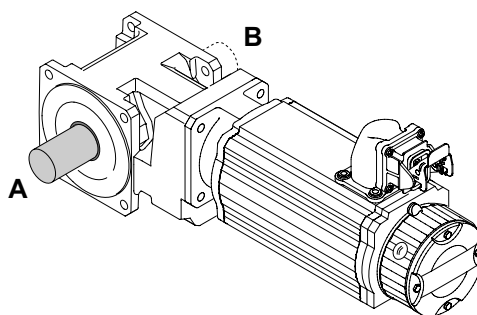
Расположение выходного вала на конических редукторах BSF..
